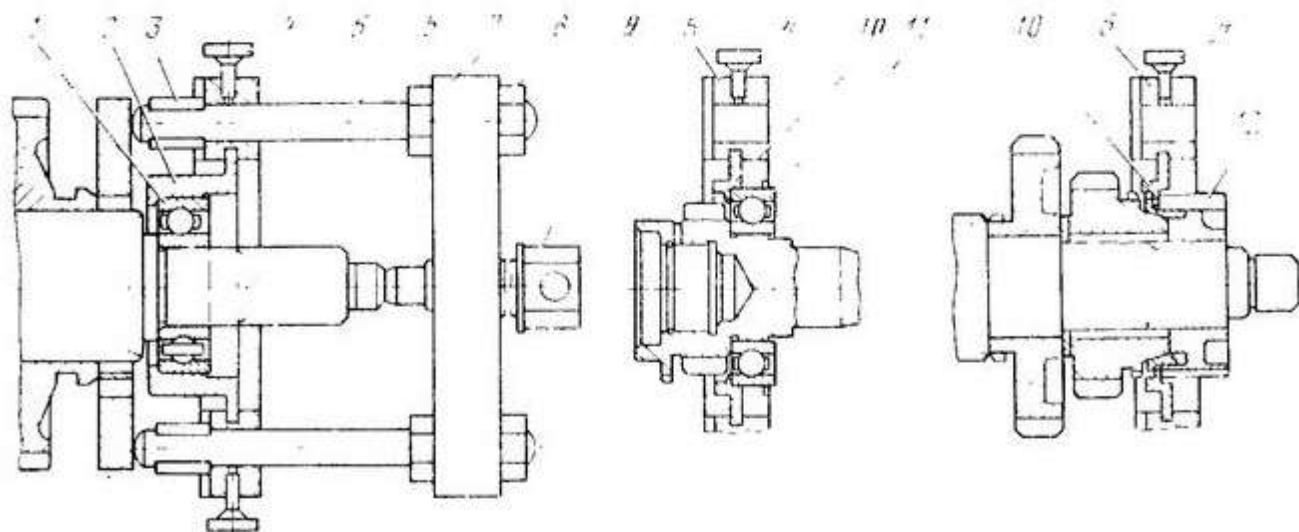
Съемник для снятия ступиц и подшипников с первичного и вторичного валов: 1 и 11—подшипники; 2 и 10—вкладыши; 3—упор; 4—винт; 5—каретка; 6—шпилька; 7—траверса; 8—гайка; 9—винт; 12—ступица
